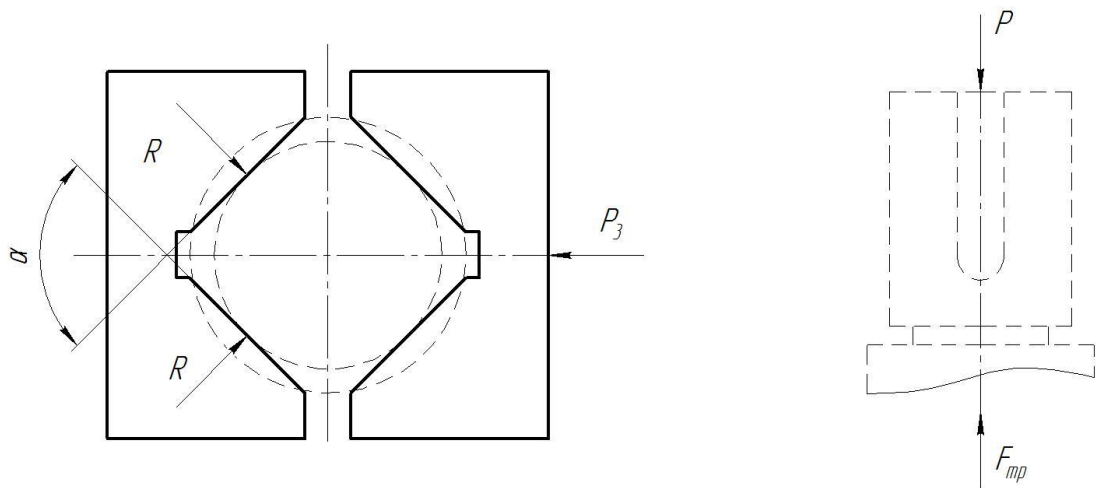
Силы, действующие в процессе обработки заготовки на шпоночно-фрезерном станке
